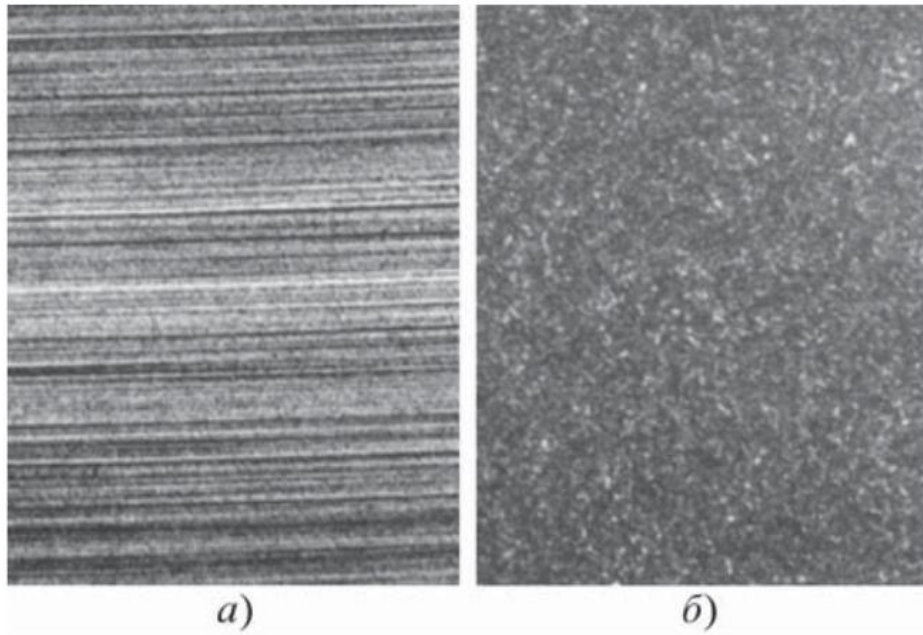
Поверхности режущих платин с оксидными пленками:
